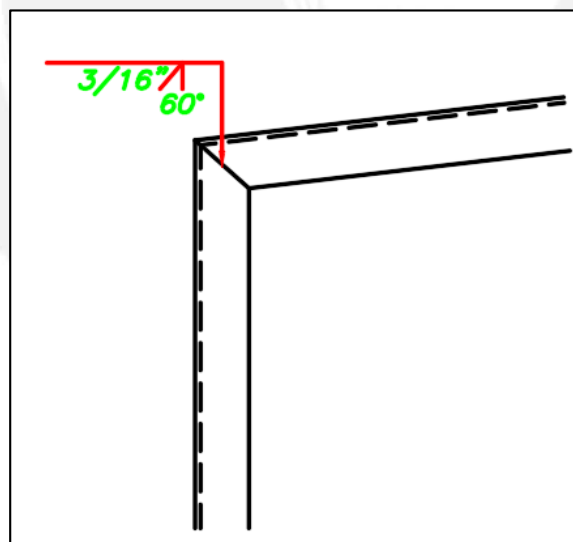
SIMBOLOGÍA DE JUNTA SOLDADA ENTRE UNIÓN BRIDA SUPERIOR Y MONTANTE
